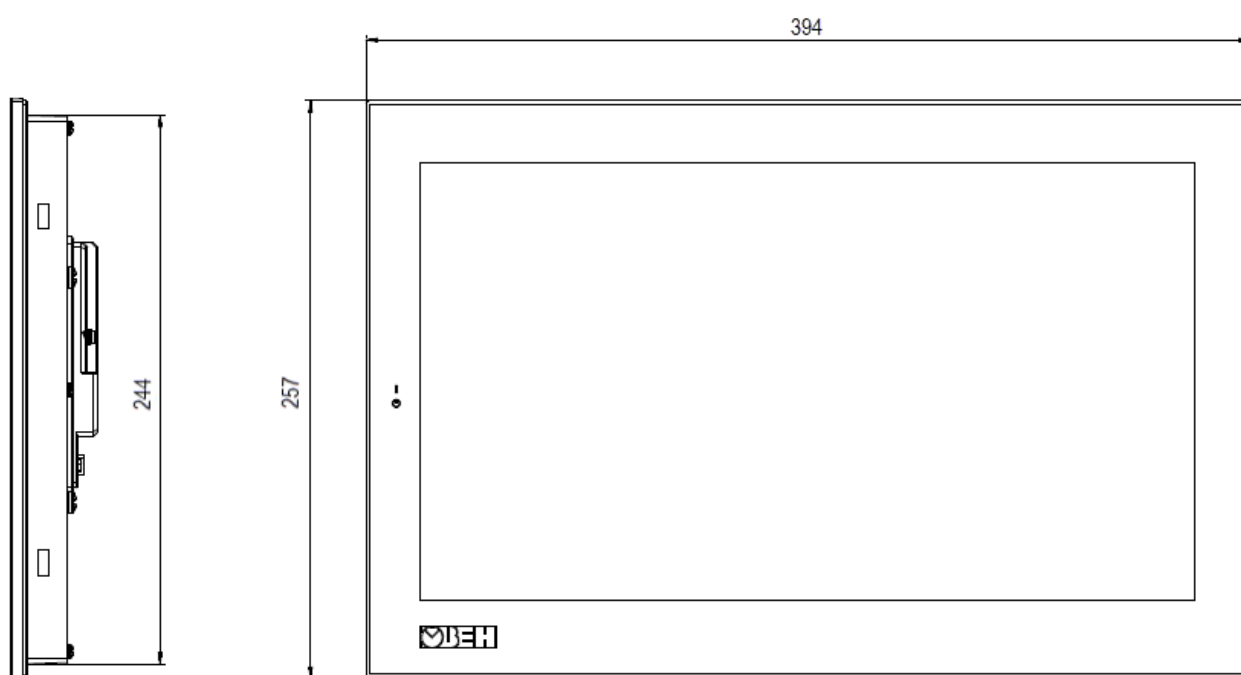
Габаритные размеры СП210-15-Р
